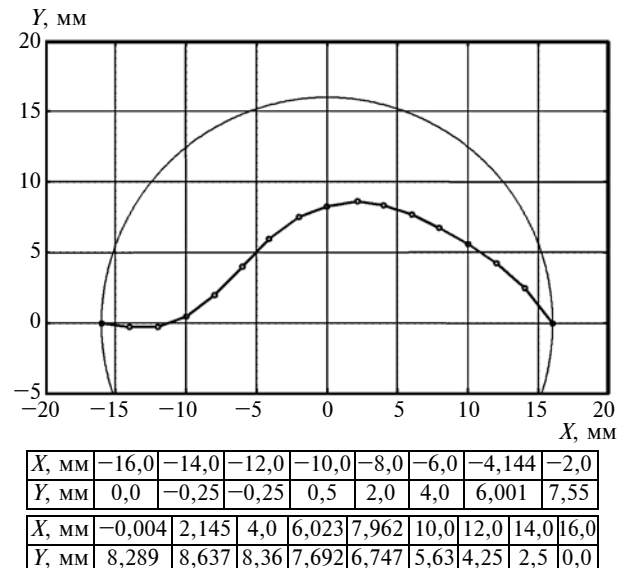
Торцевой профиль винтовой канавки двузубой концевой фрезы
